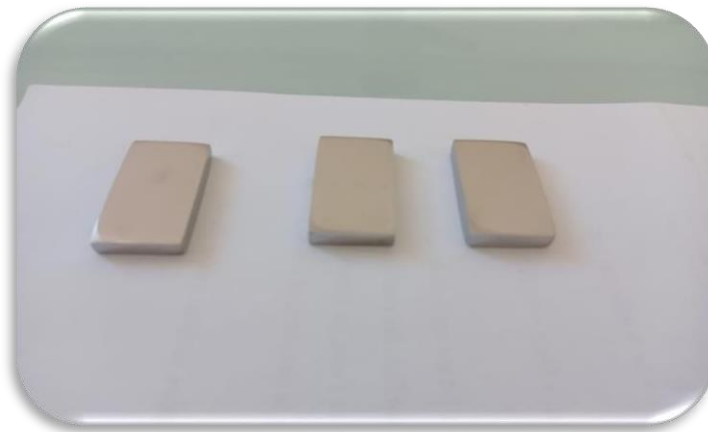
les dimensions et la forme des plaquettes de l'acier
